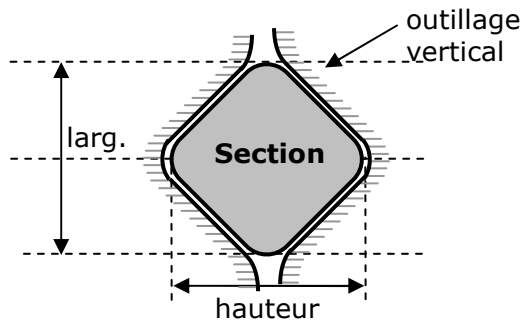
Section de la barre APRES la passe de laminage pour le cas de cylindres verticaux
